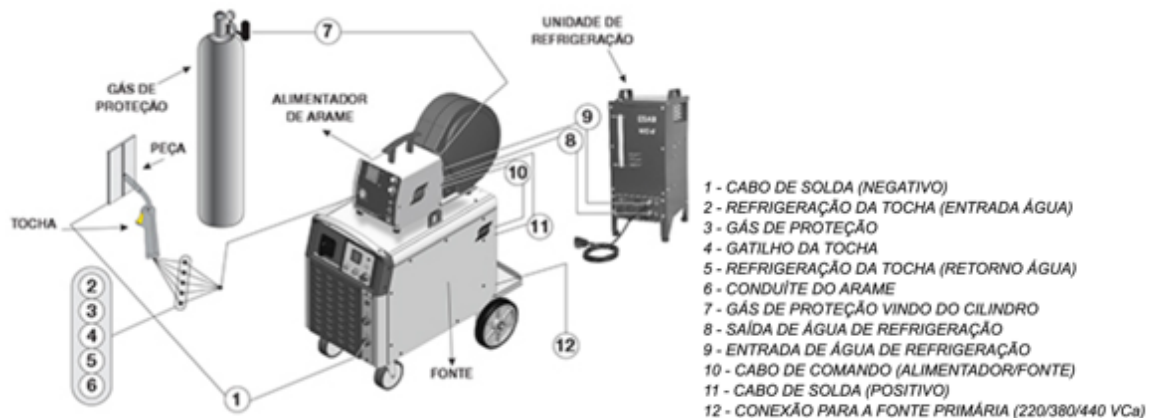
Equipamentos para soldagem MIG/MAG (ESAB, 2022)
